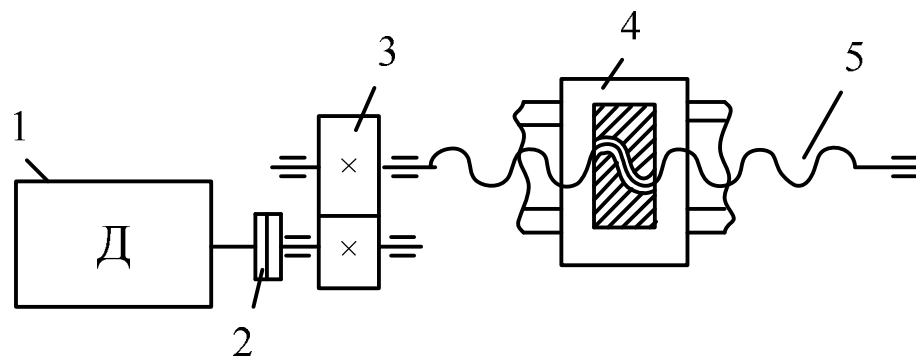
Кінематична схема приводу подачі токарного верстату
